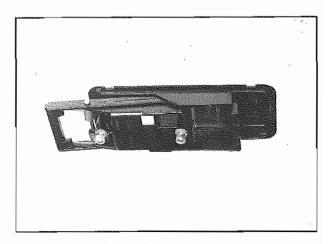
Viti fisseggio maniglia Screws fixing handle
